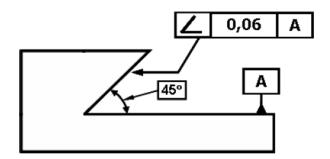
Indicação de tolerância de inclinação em desenho técnico
